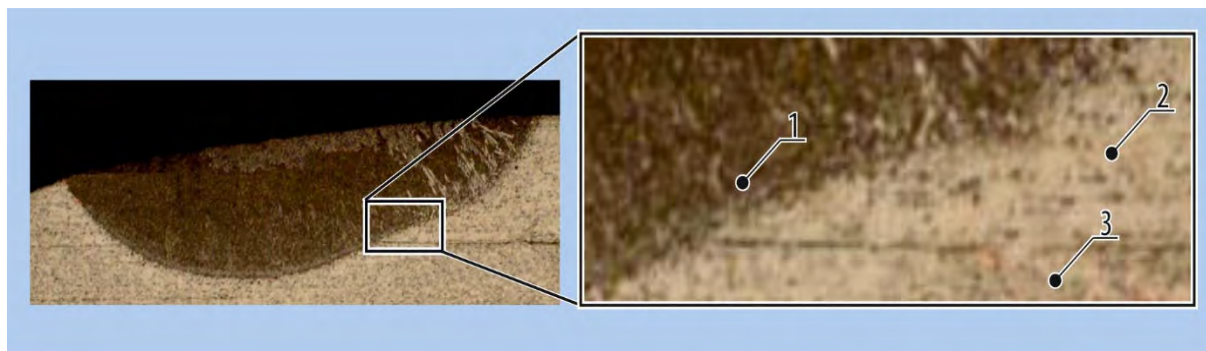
Структура сварного шва при силе тока 40–44 А: 1 — сварной шов, 2 — оболочка, 3 — заглушка
